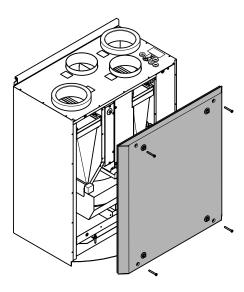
Smontaggio / montaggio dell'anta frontale interna
